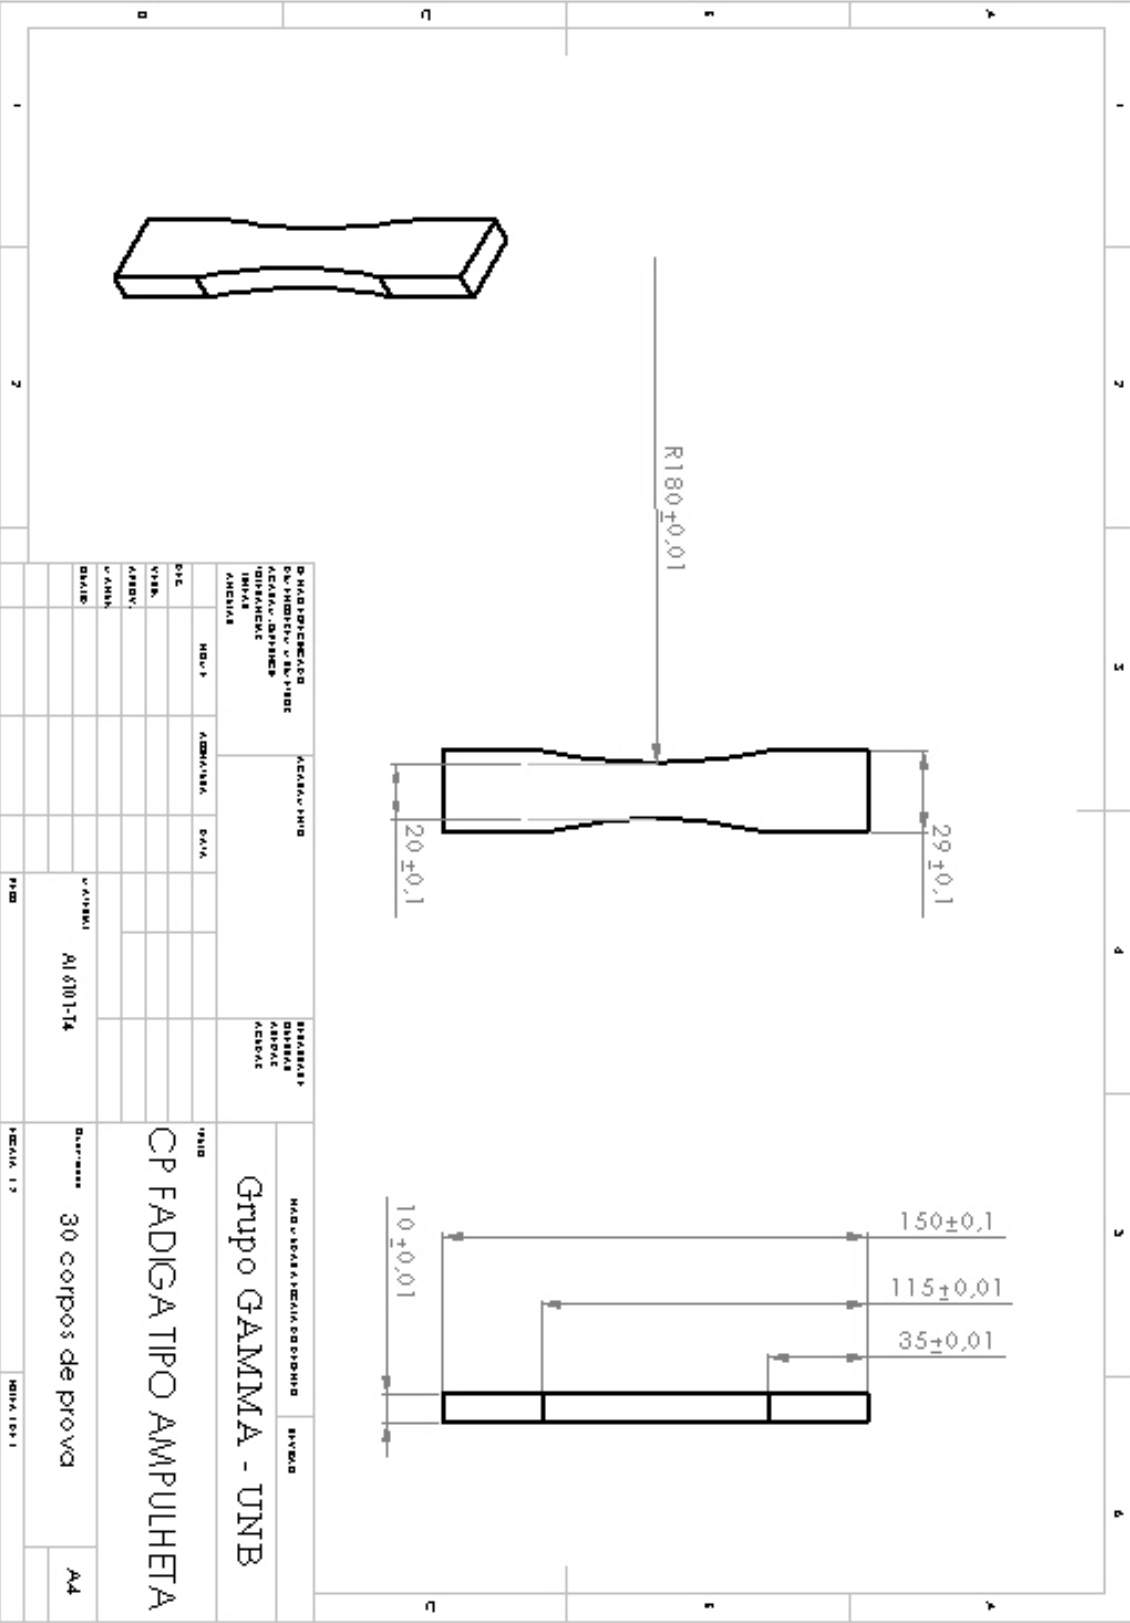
Desenho técnico do corpo de fadiga uniaxial.
